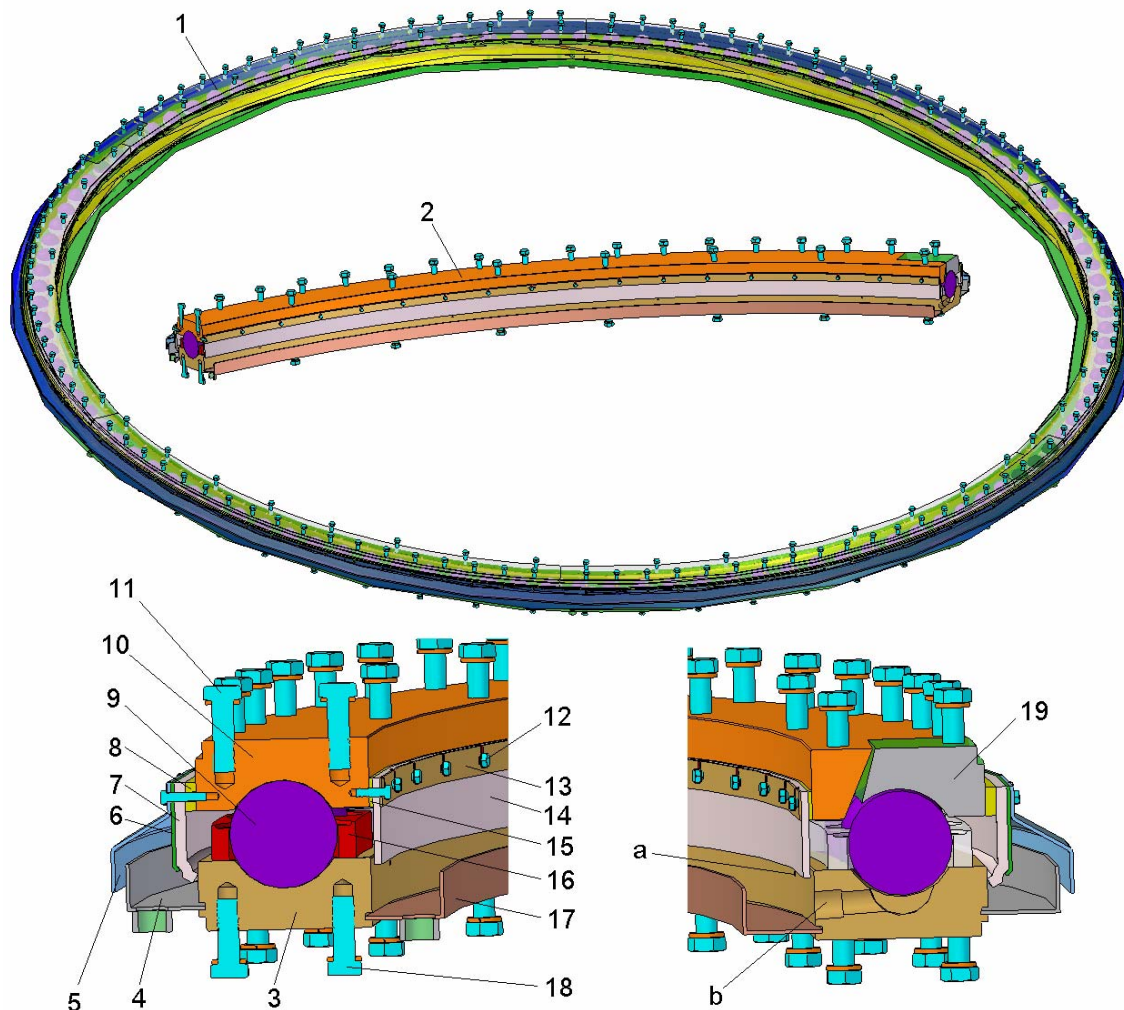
Rulment axial cu bile cu diametrul de rulare de 8650 mm
